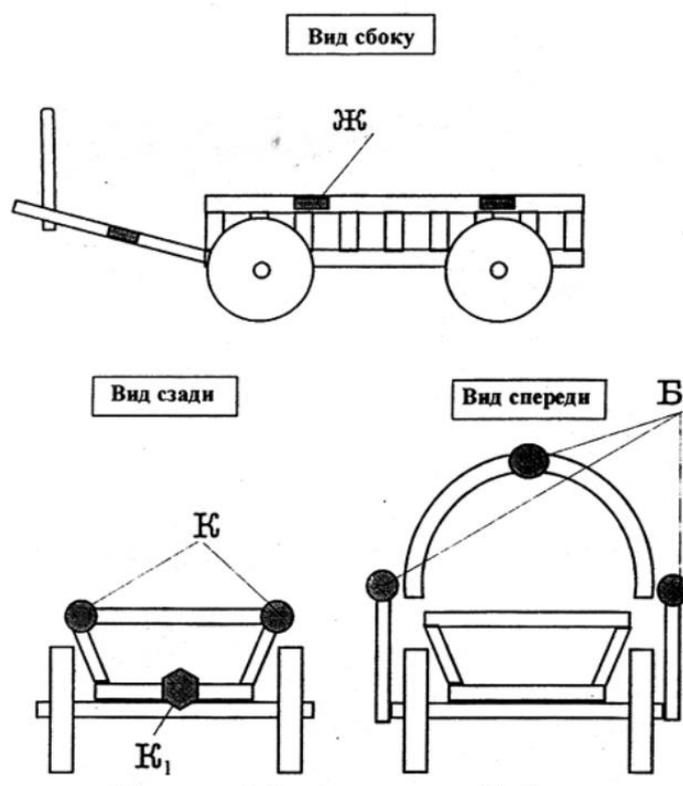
Схема установки световозвращающих элементов (световозвращающая пленка по СТБ 1140-99) Ж – желтый; К – красный круглый; К1 – красный шестиугольный; Б – белый.
